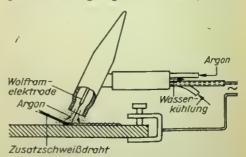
/2-5 Wolfram-Inertgas- (WIG-) Schweißen
